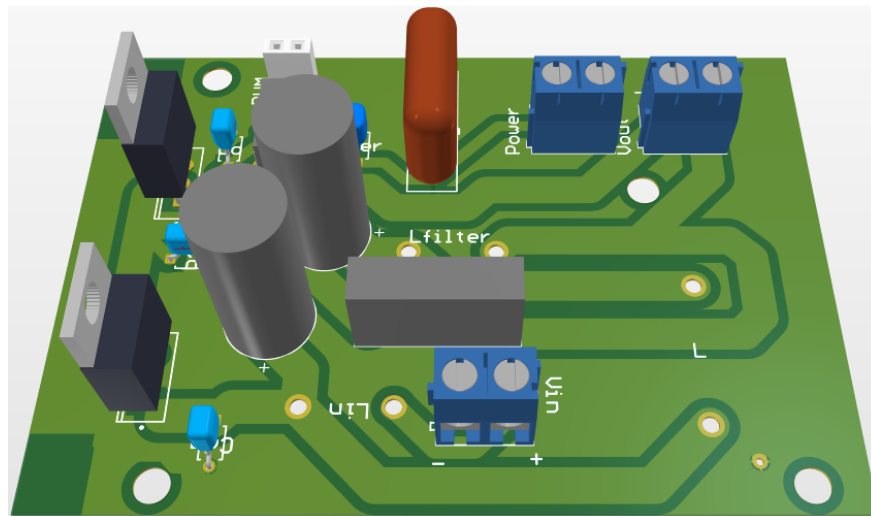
Vista 3D de diseño de PCB del convertor DC-DC
